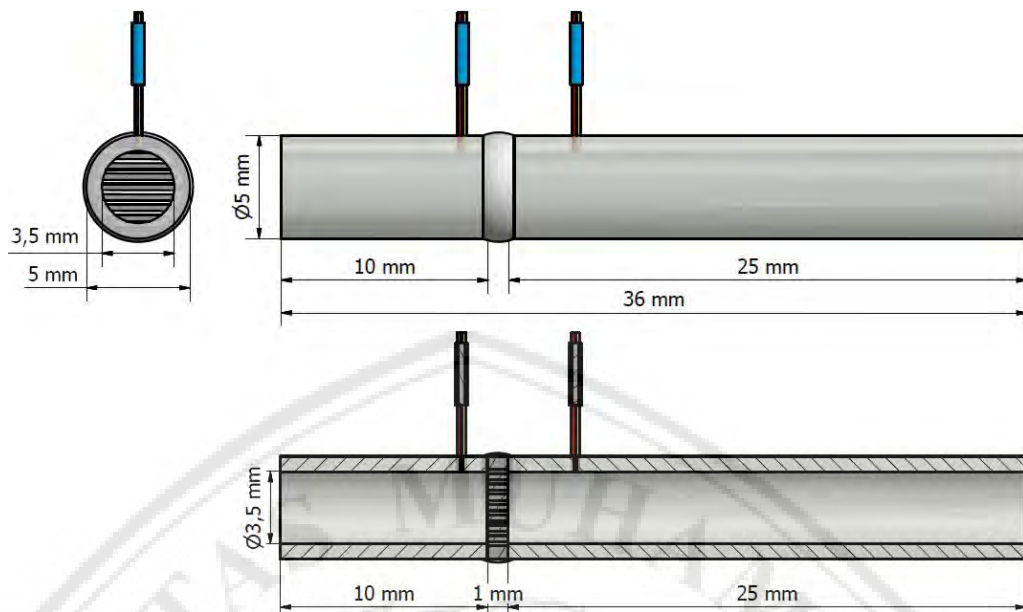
Dimensi *mesoscale – combustor flame holder wire mesh 60* (Skala 2,5x).
